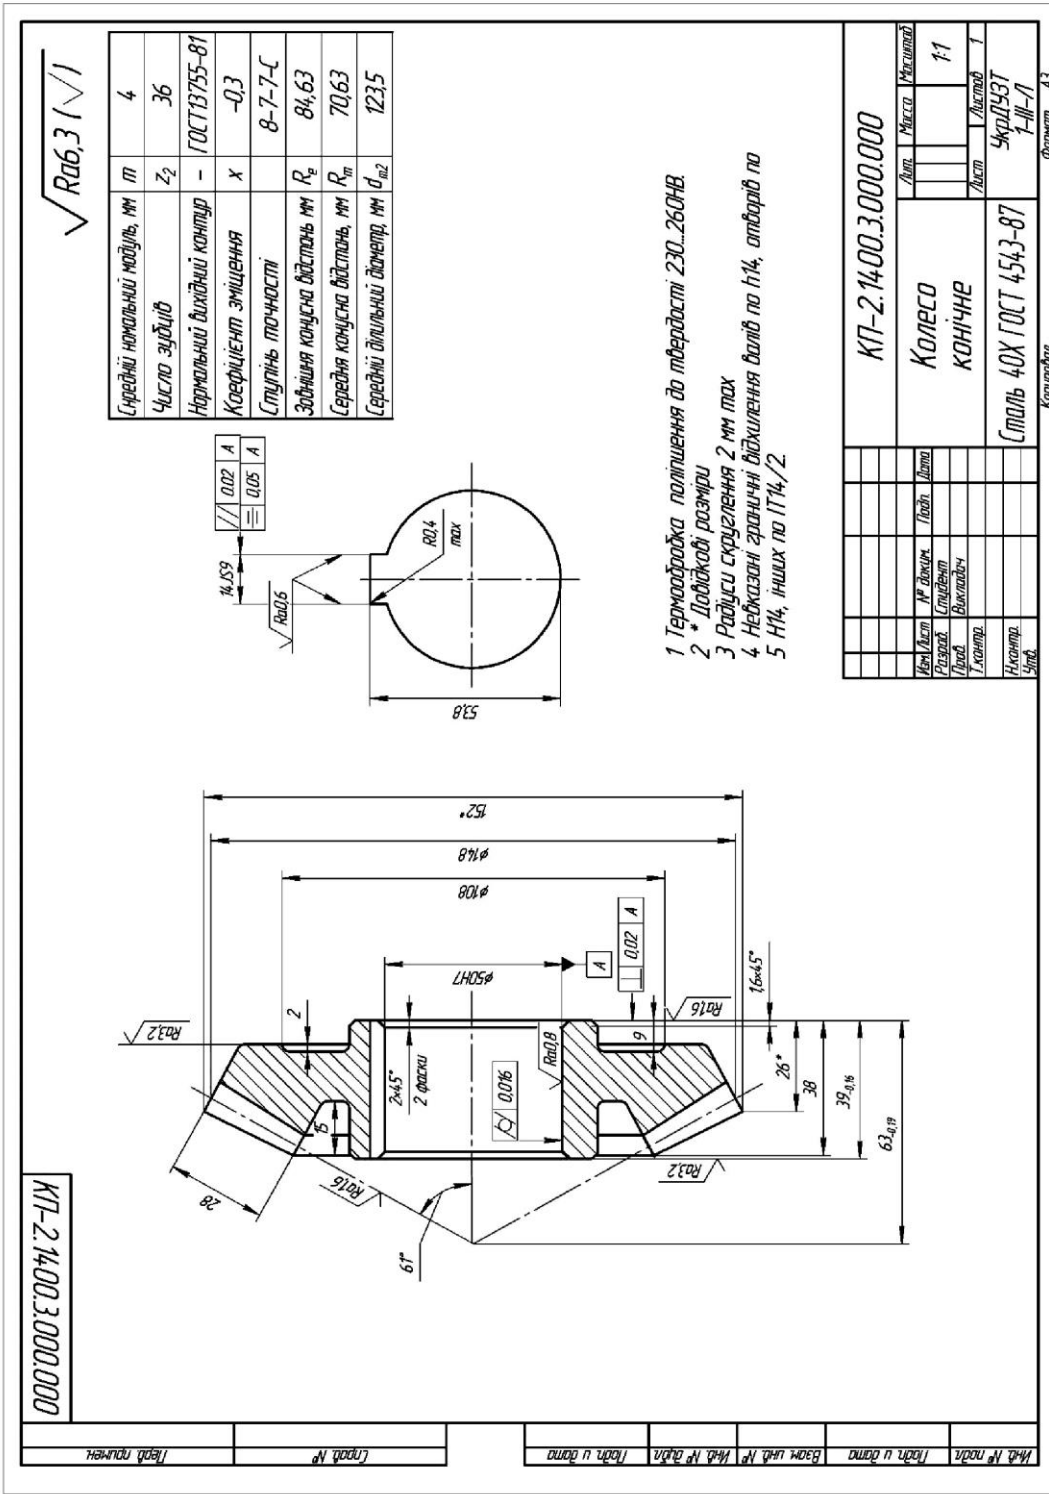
Робоче креслення конічного зубчастого колеса
